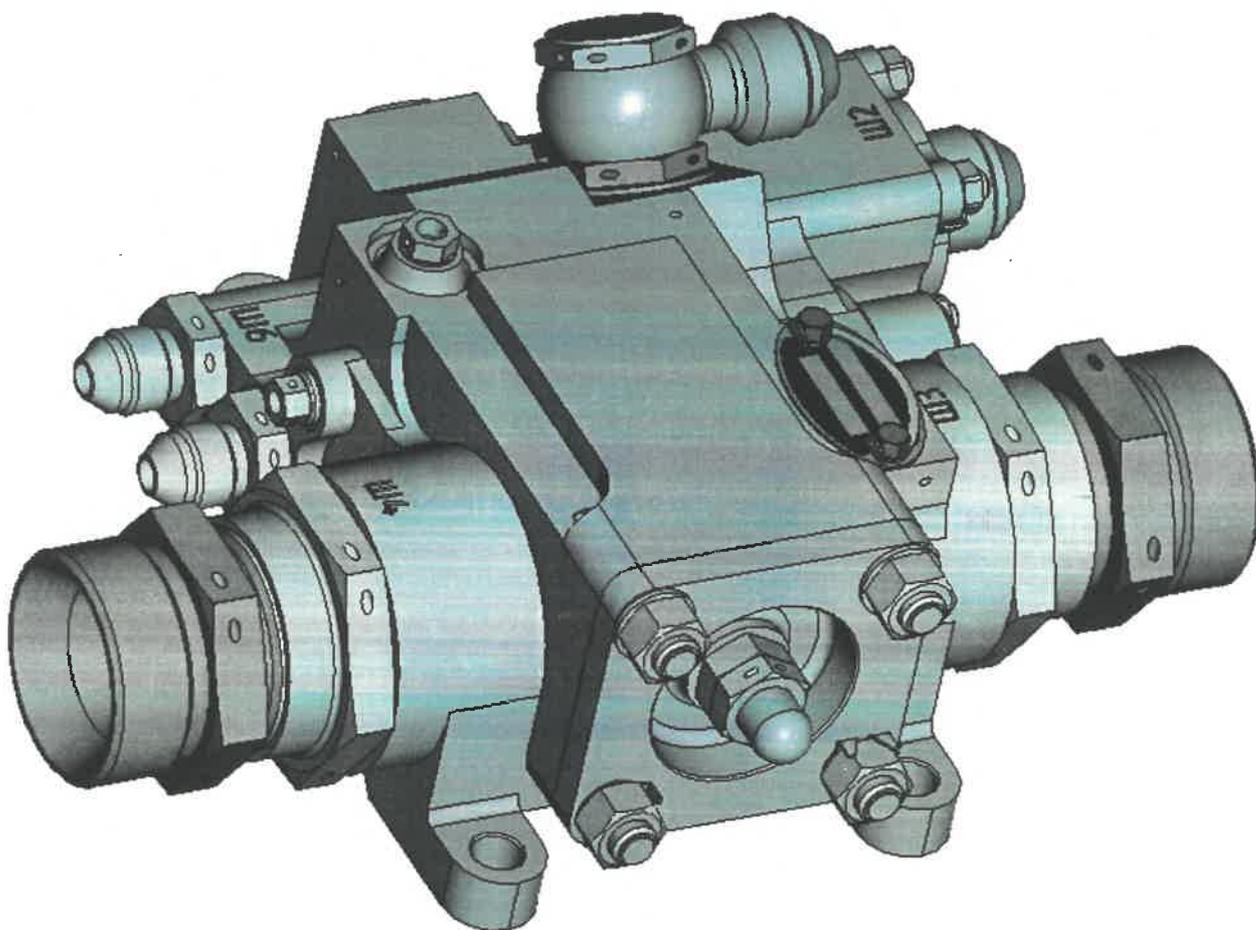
Общий вид агрегата перепуска топлива АПТ-80.
